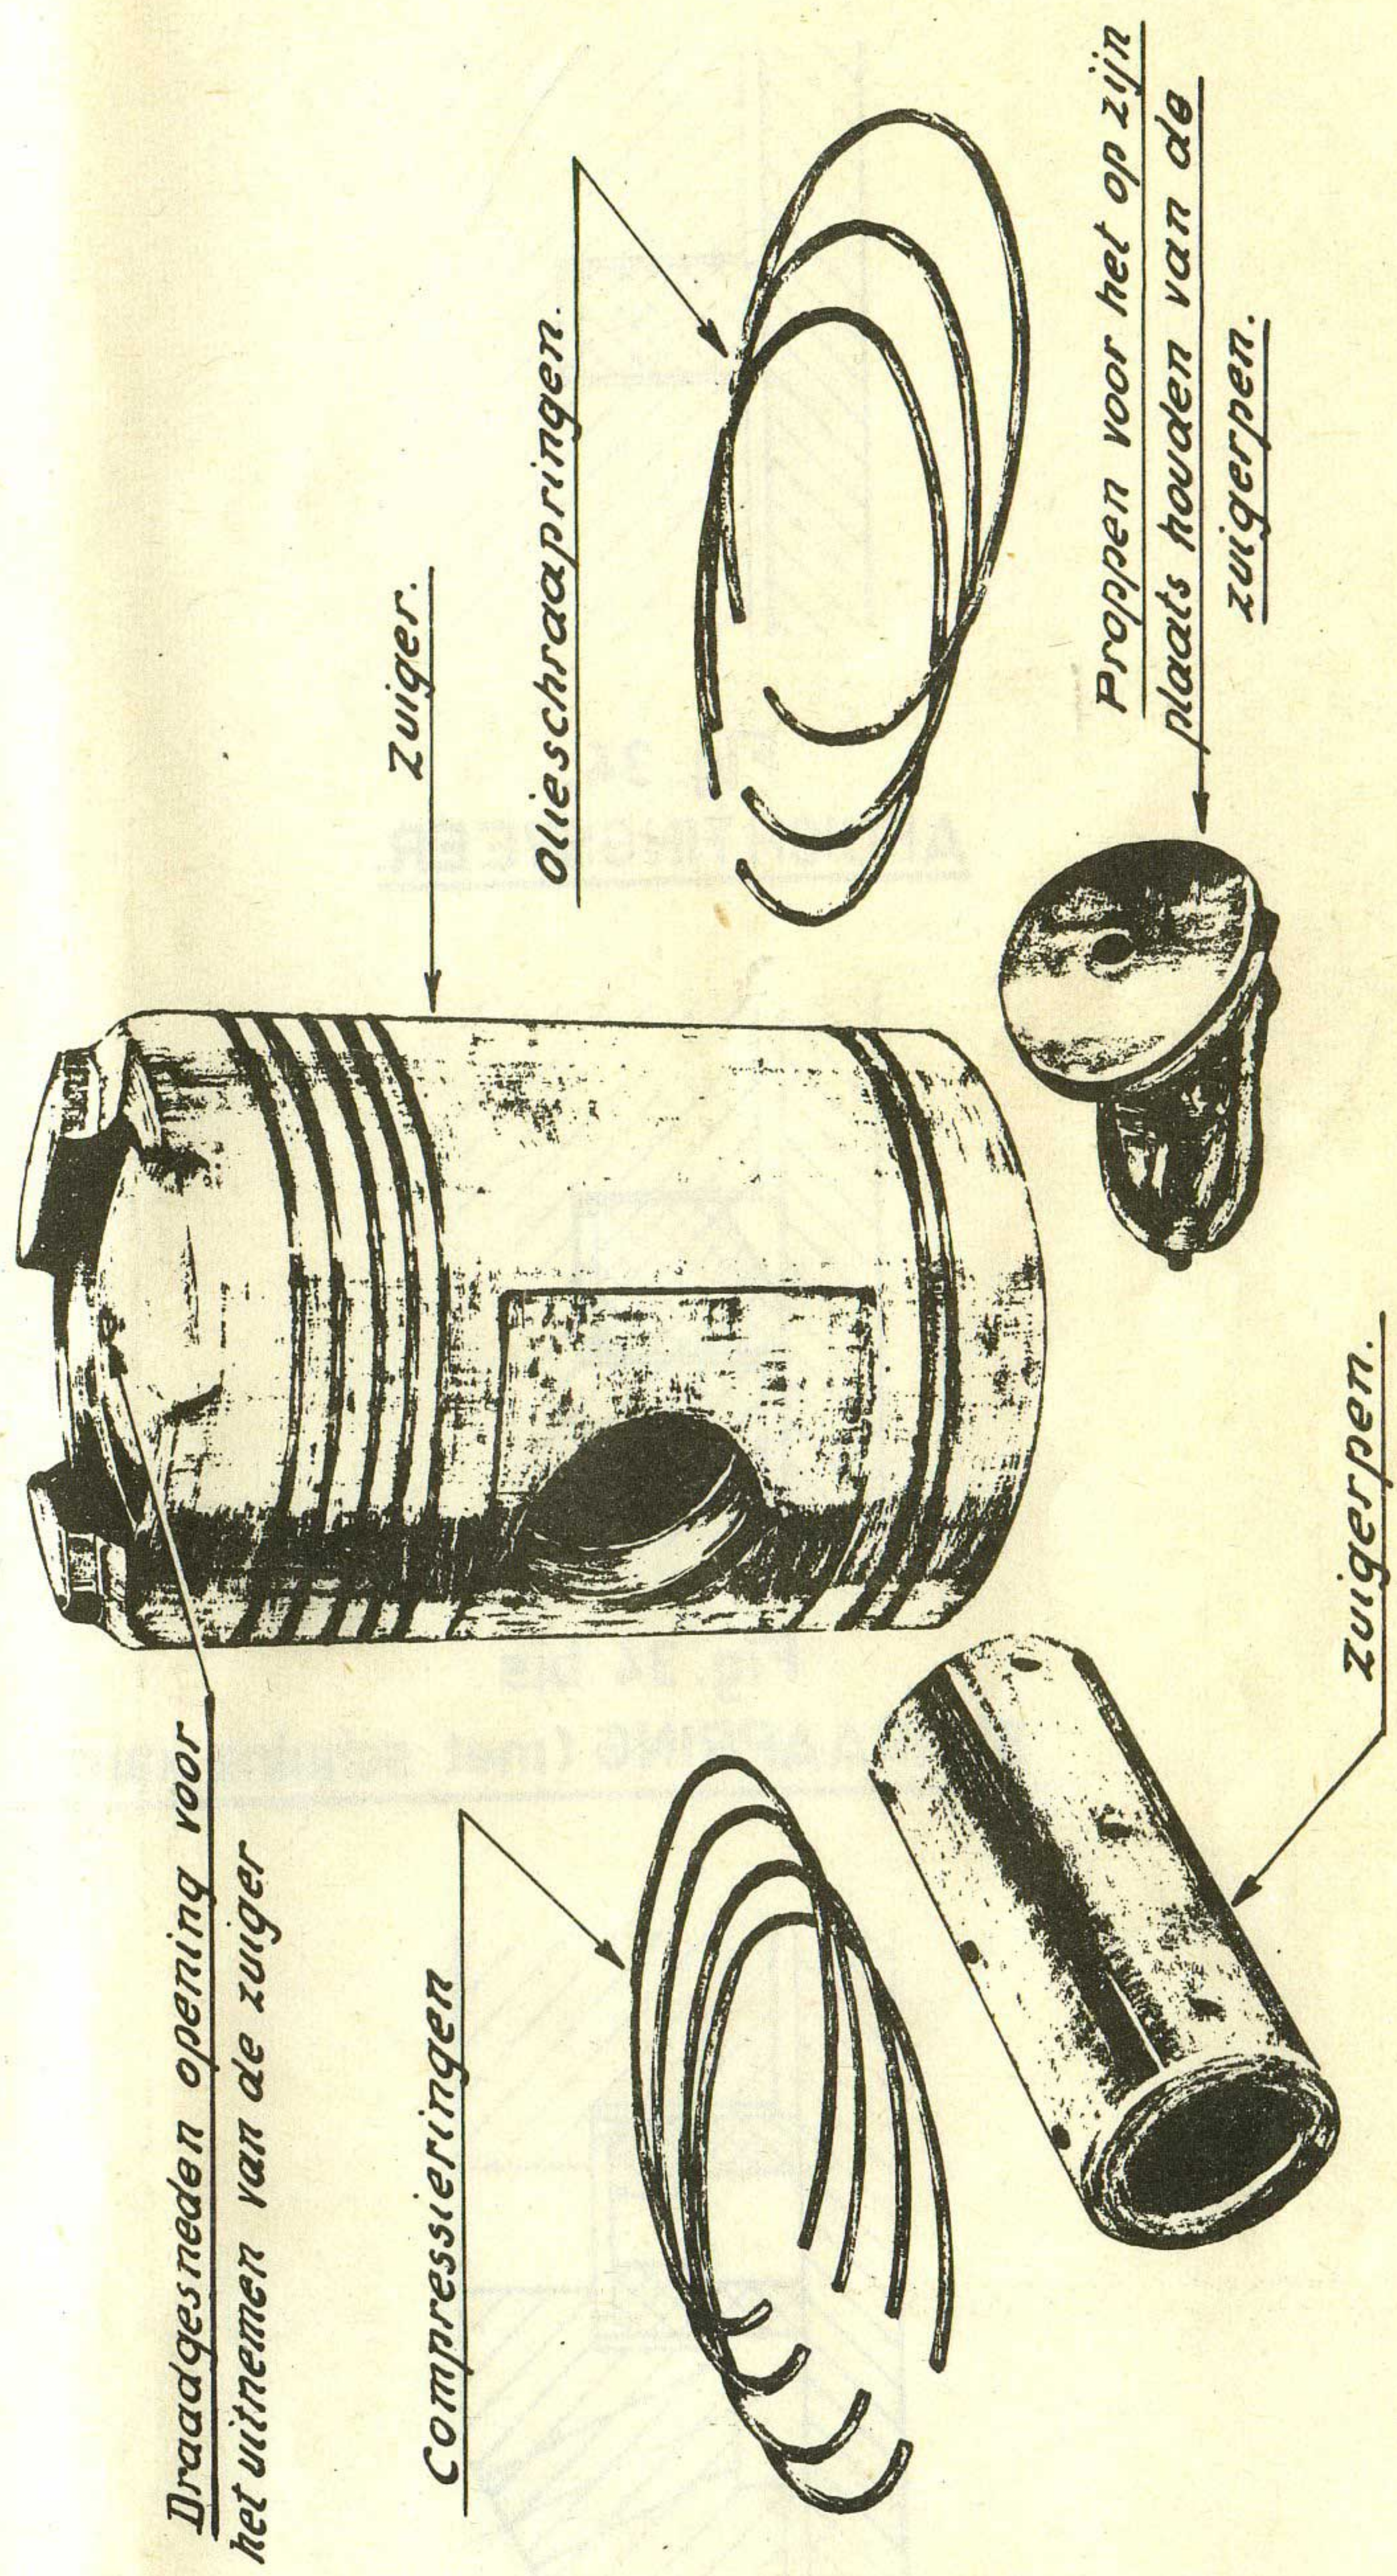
ZUIGER EN RINGEN VAN DE BALDWIN - MOTOR.
